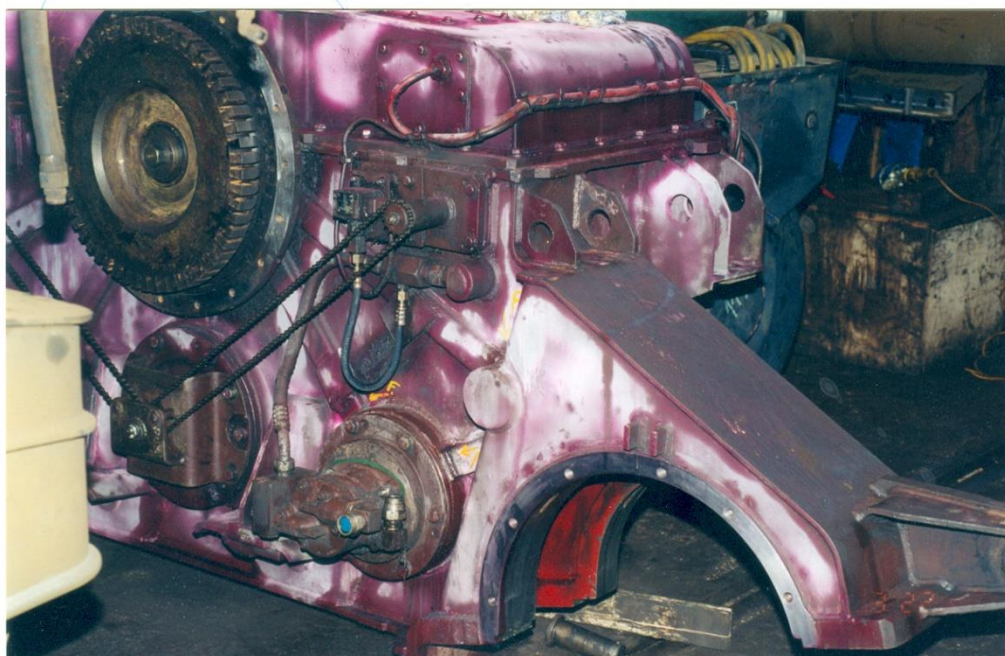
Conjunto Corpo e Tampa sujeitos a um ensaio não-destrutivo com líquidos penetrantes [Imagem cedida por cortesia da Professora Teresa Morgado].
